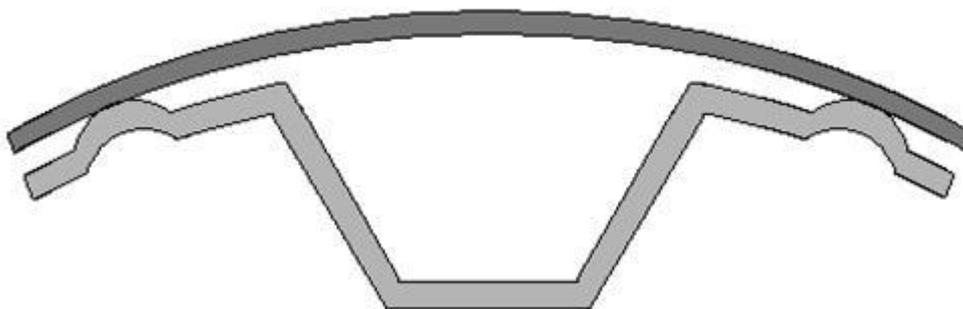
Configuration typique pour l'utilisation du soudage par bossage
